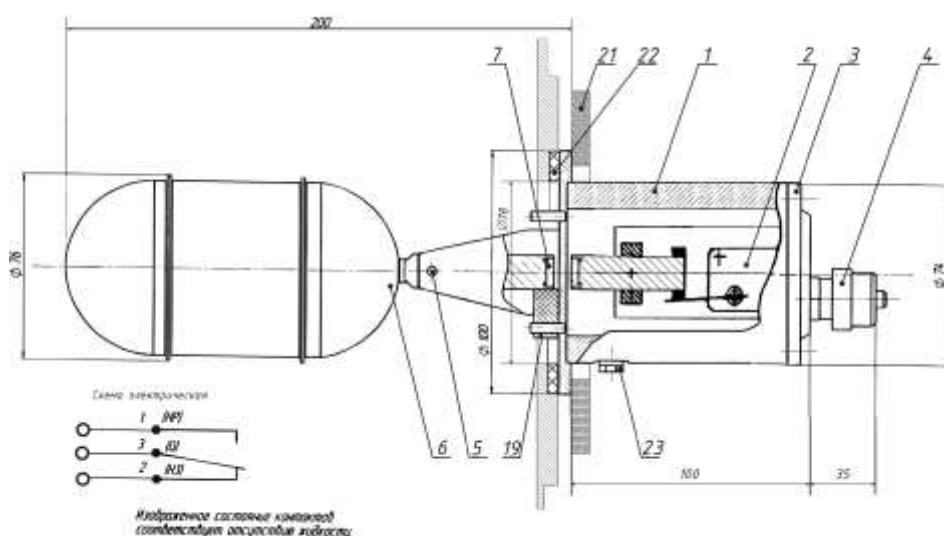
Габаритные и присоединительные размеры РОС 400-7
